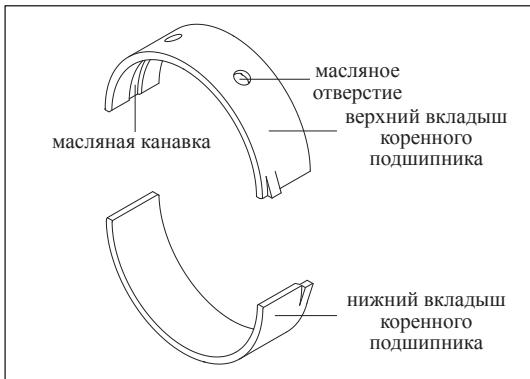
Верхний и нижний вкладыши коренного подшипника
